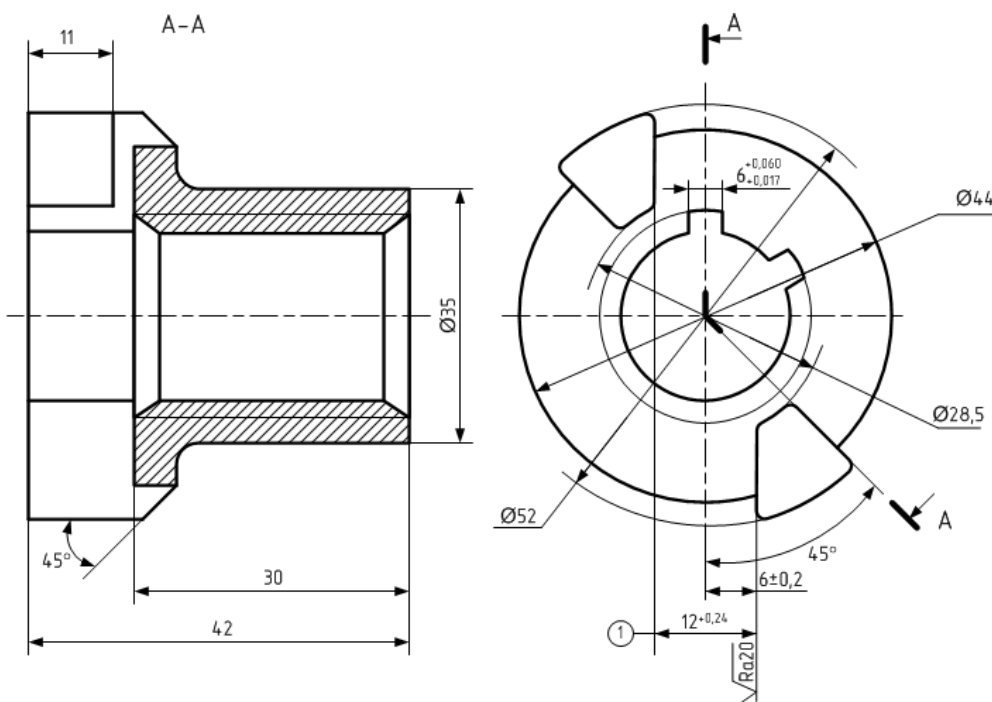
Кулачковая муфта привода гидронасоса двигателя СМД
